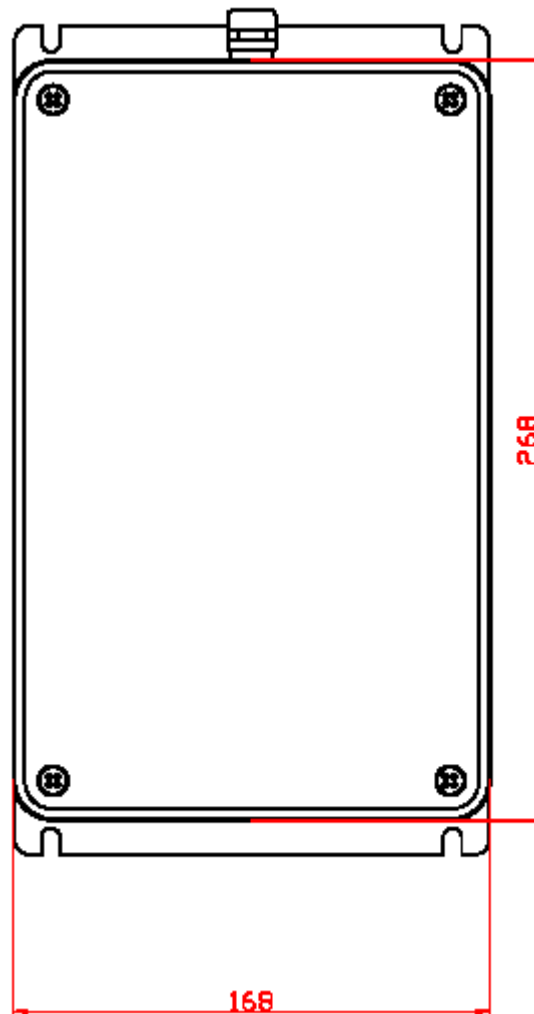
Регенератор во влагозащищенном корпусе. Вид сверху
